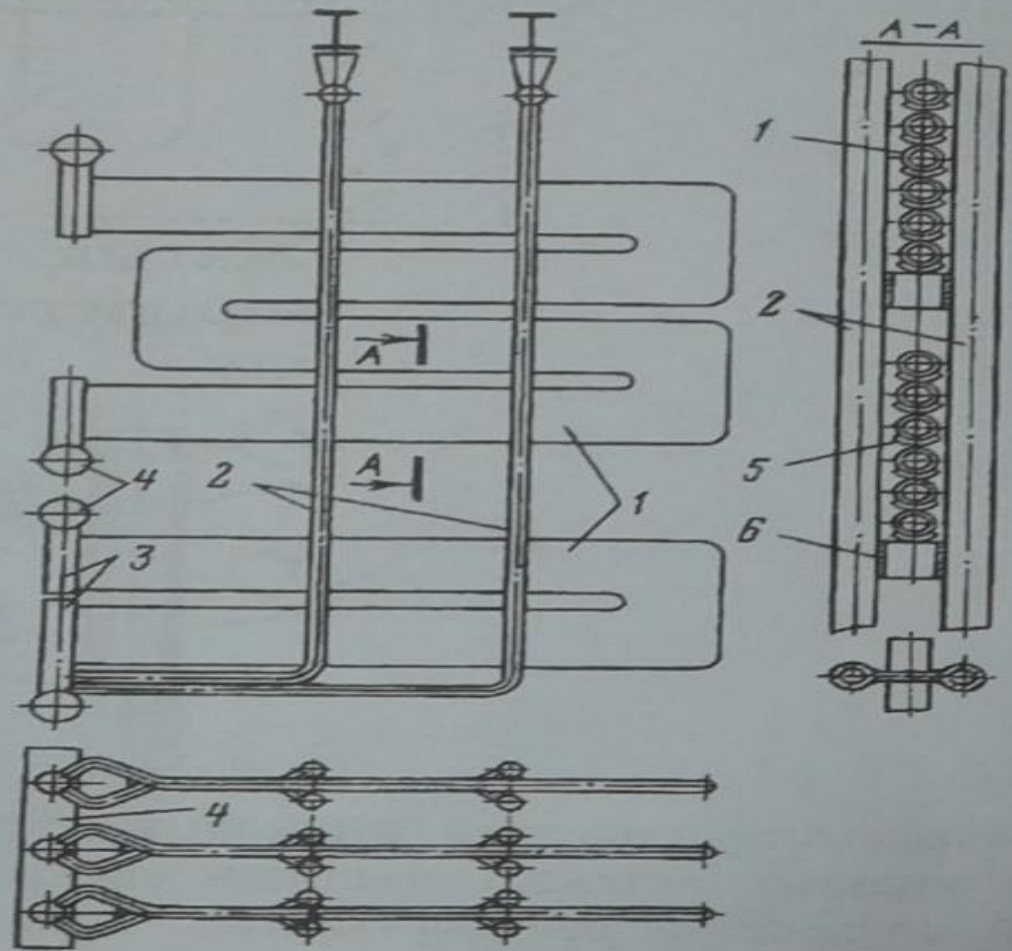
Сборка блока пароперегревателя котла ГМ-50-14:
